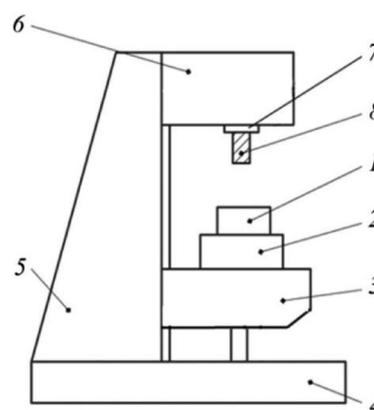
Компановка ТС: 1 – заготовка; 2 – приспособление; 3 – консольный стол; 4 – основание; 5 – стойка; 6 – шпиндельная бабка; 7 – шпиндель; 8 – инструмент
